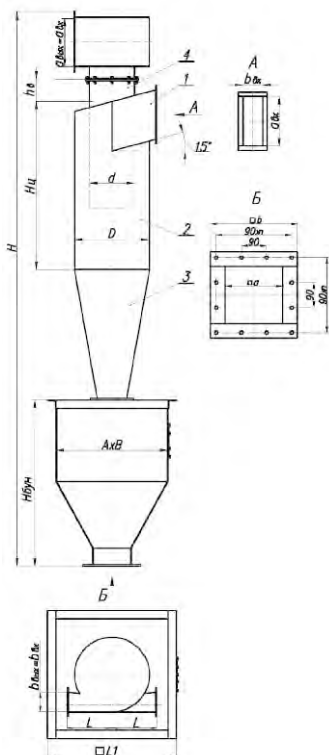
Общий вид. Габаритные и присоединительные размеры ЦН-15 -1УП.
